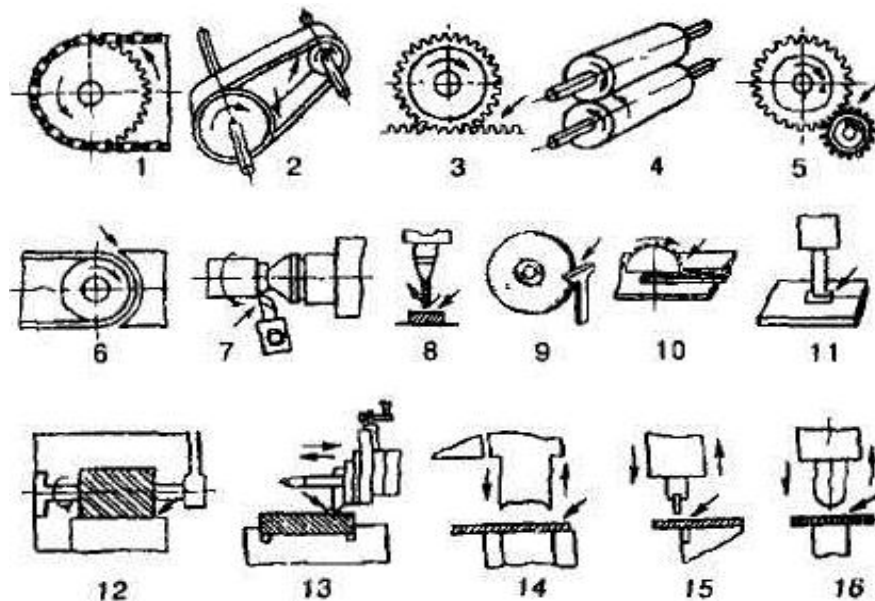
Загальний вигляд небезпечних зон у машинобудуванні: 1 – ланцюгова передача; 2 - пасова передача; 3,5 – зубчата передача; 4 - вали; 6 - конвеєр; 7 – токарний верстат; 8 – свердління; 9 – абразивний круг; 10, 11, 15 - пила; 12 – фрезерування; 13 – поперечне стругання; 14 – штампування; 16 – гнуття.
